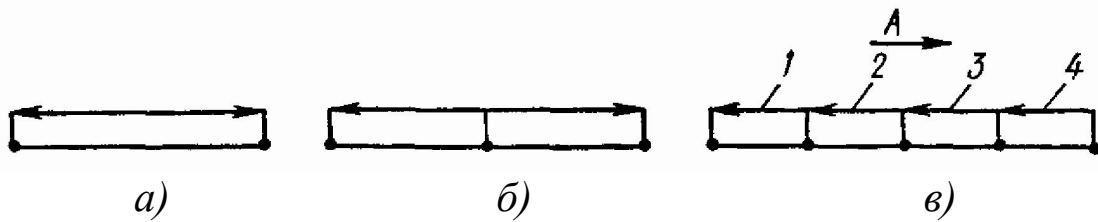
Схемы сварки: *a* – на проход; *б* – от середины к краям; *в* – обратноступенчатым способом; *A* – общее направление сварки; *1–4* – последовательность сварки участков
